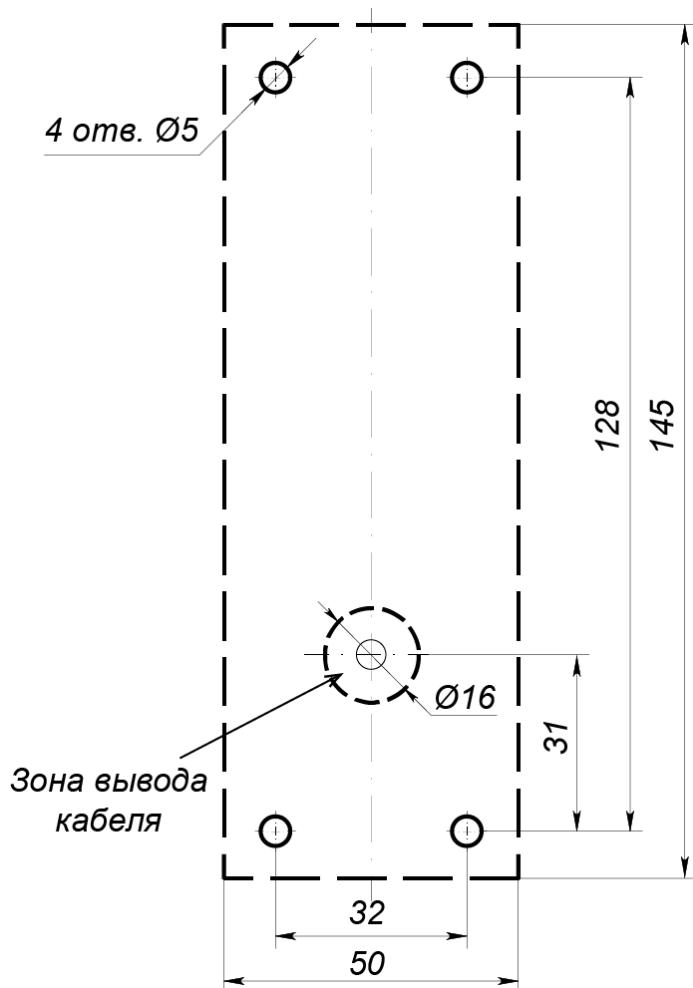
Разметка отверстий для установки считывателя (пунктиром показаны габариты корпуса считывателя)
